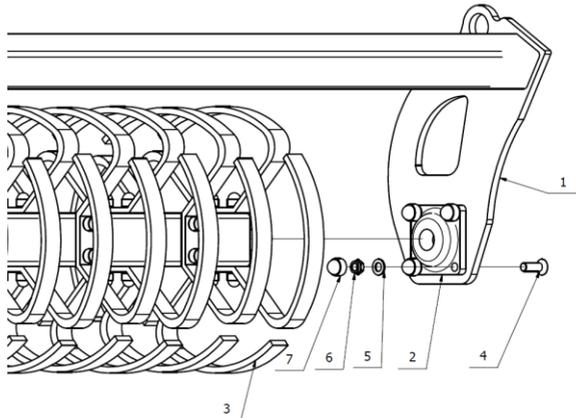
Ø500mm Ringwelle - Lagermontage.
